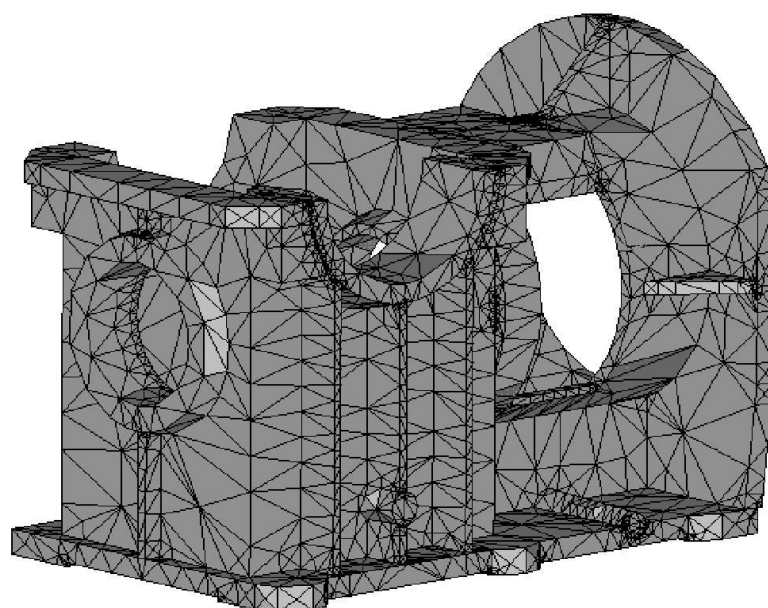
Расчетная модель корпуса редуктора (использование базисных конечных элементами типа “пирамида”)
